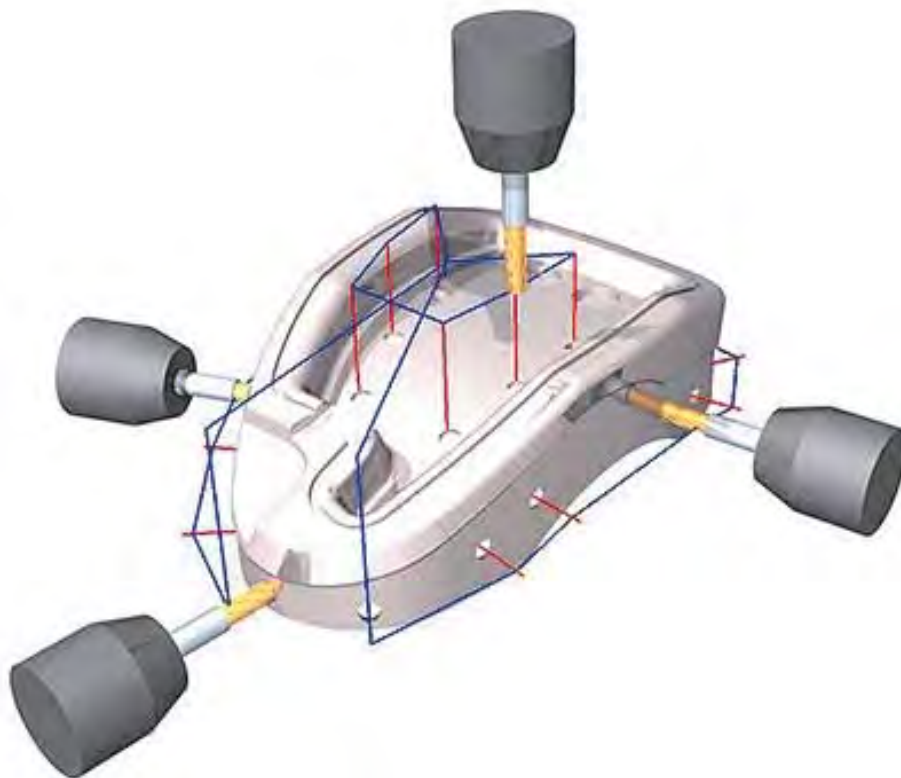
Обработка отверстий в корпусной детали на многоцелевом станке
